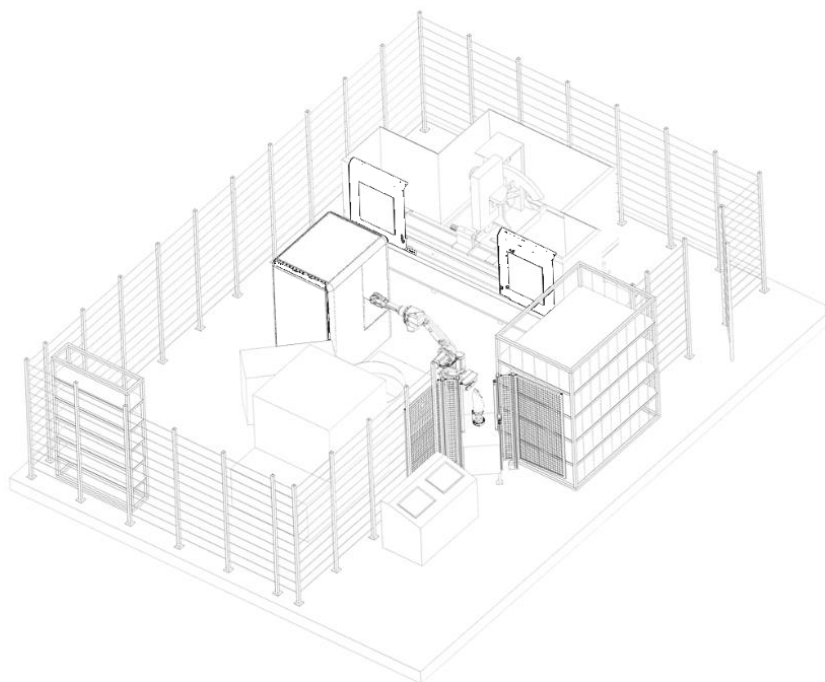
Компоновка роботизированного комплекса шлифовки лопаток ГТД
